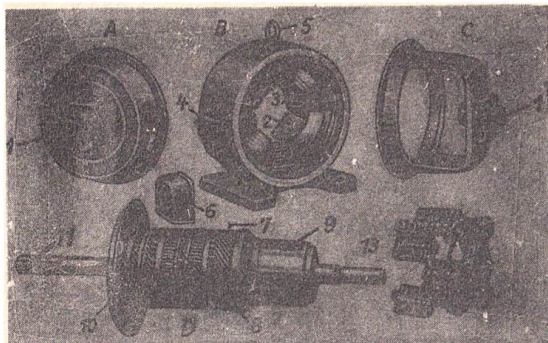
Aufbau einer Gleichstrommaschine mit Schildlager
